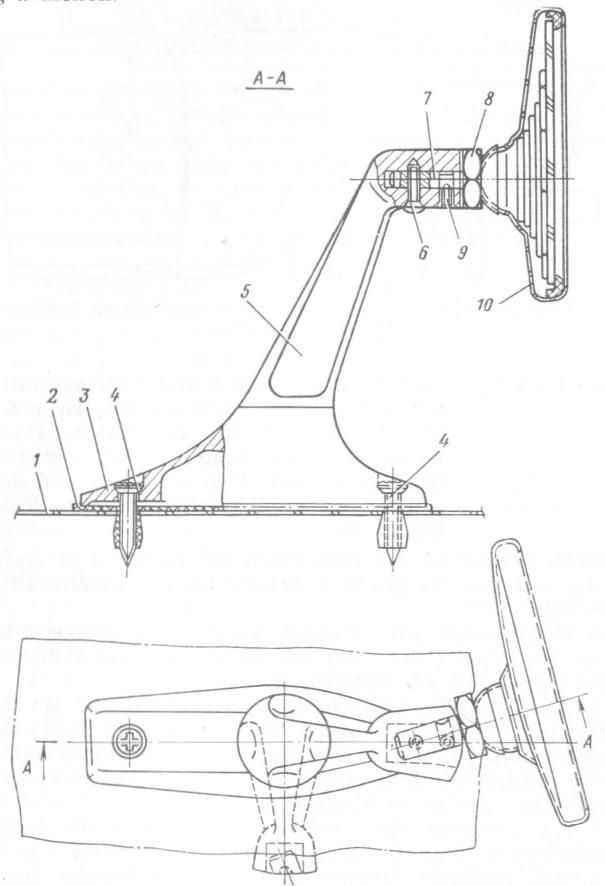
Außenspiegel und Teile zu dessen Befestigung an Karosserie (Erklärung der Positionsnummern siehe im Text).
